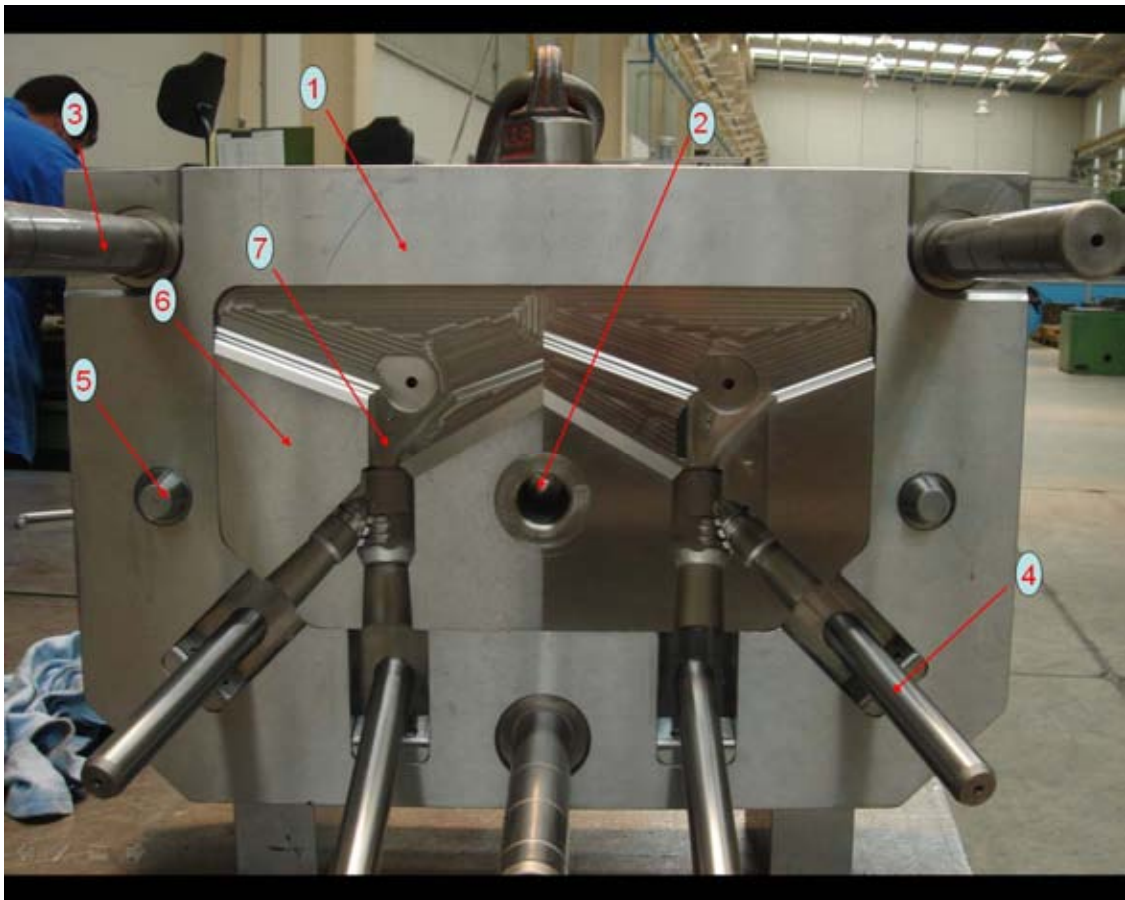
Muestra las partes del molde cavidad fija [2].
